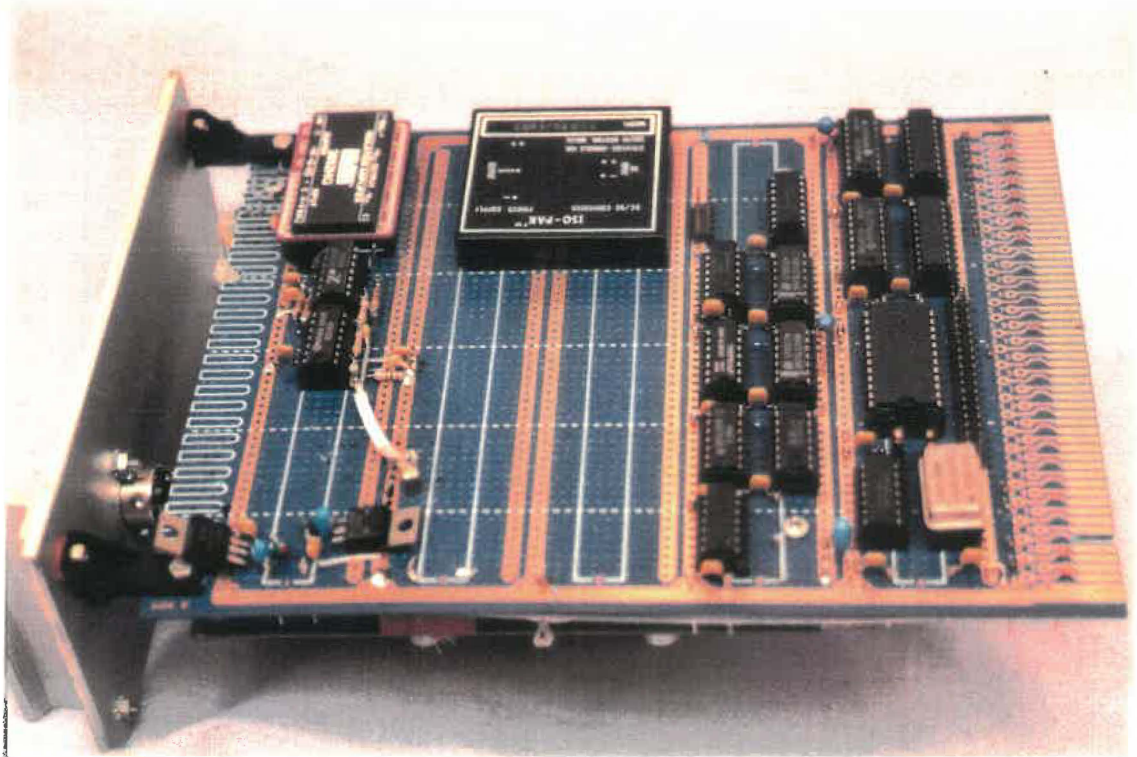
Photographie du côté recto de la carte d'acquisition.
